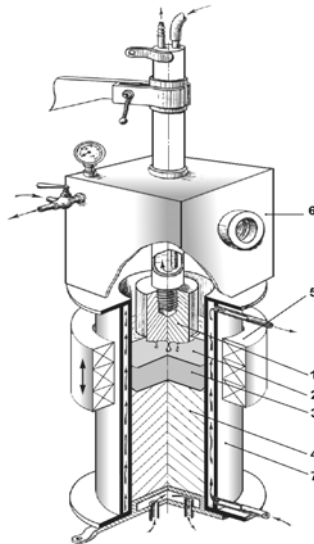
Установка МЕР [3]: 1 – витратний електрод; 2 – рідкий шлак; 3 – ванна розплавленого метала; 4 – зливоч; 5 – пристрій електромагнітного впливу; 6 – вакуумна камера; 7 – водоохолоджуваний кристалізатор.
